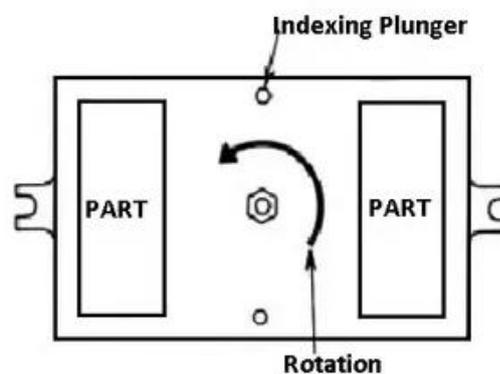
Komponen Fixture Indexing* (Hilman, 2019)
